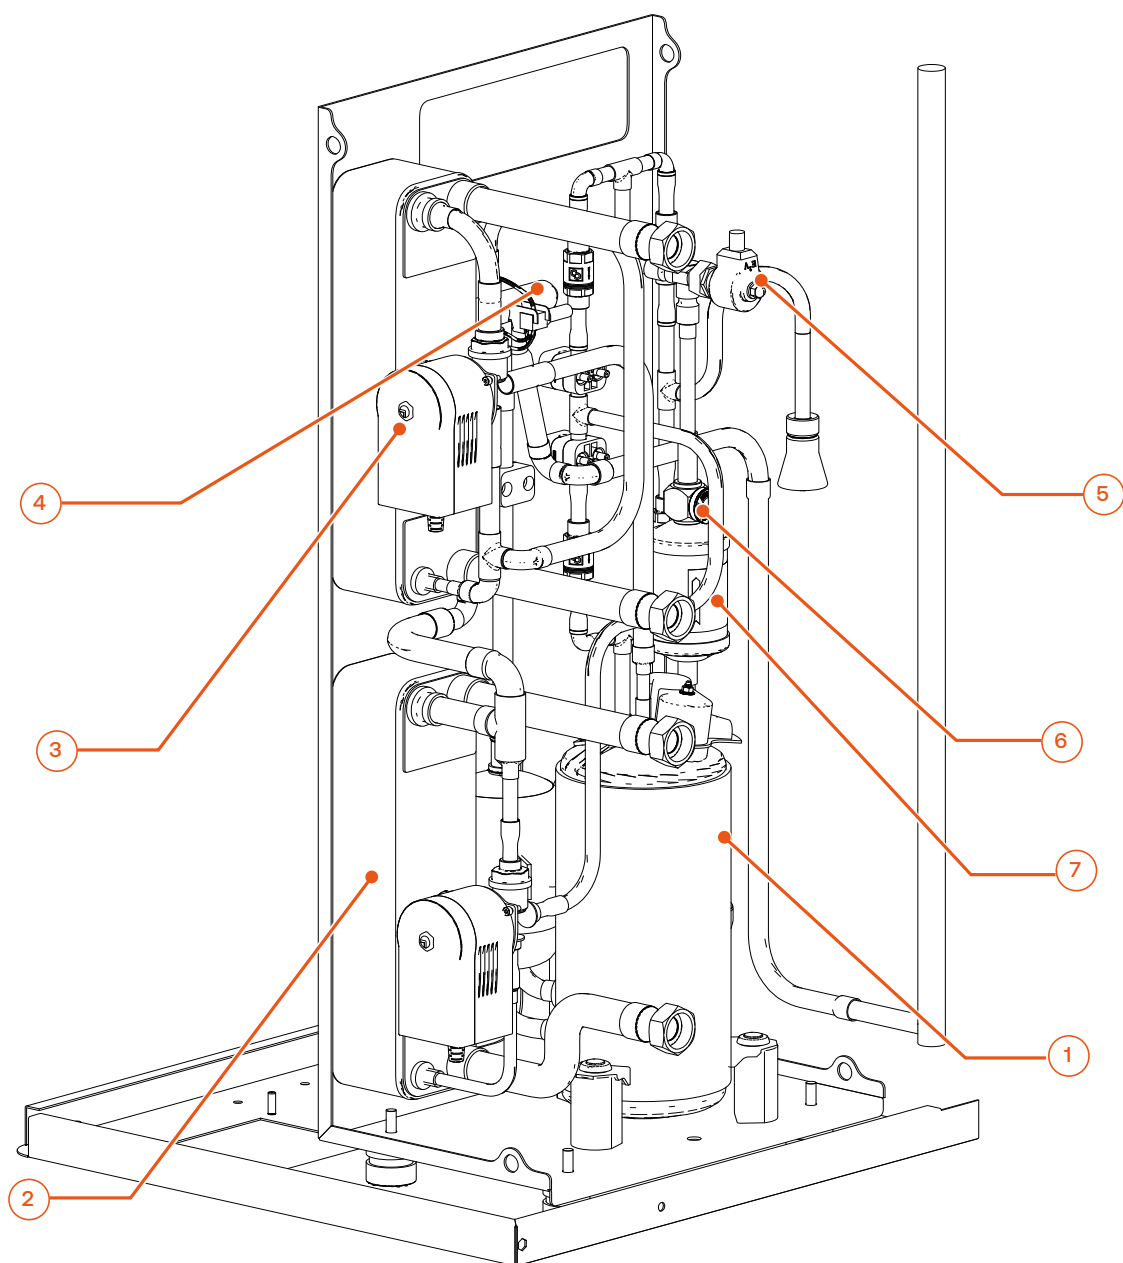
Bomba de calor - Componentes principales de un sistema de 4 tubos
